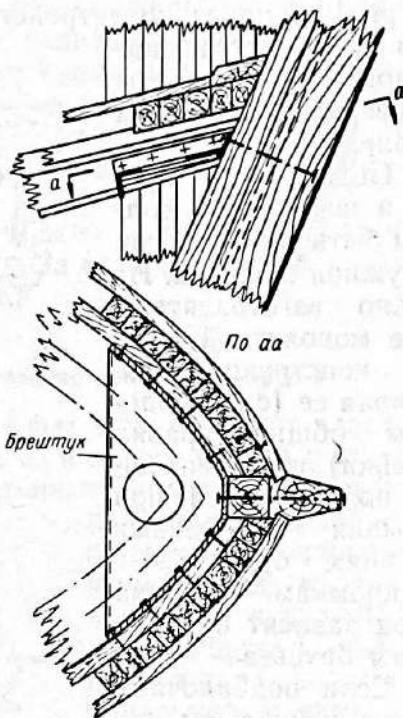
Крепление подбалочных брусьев к форштевню брештуком сварной конструкции.
